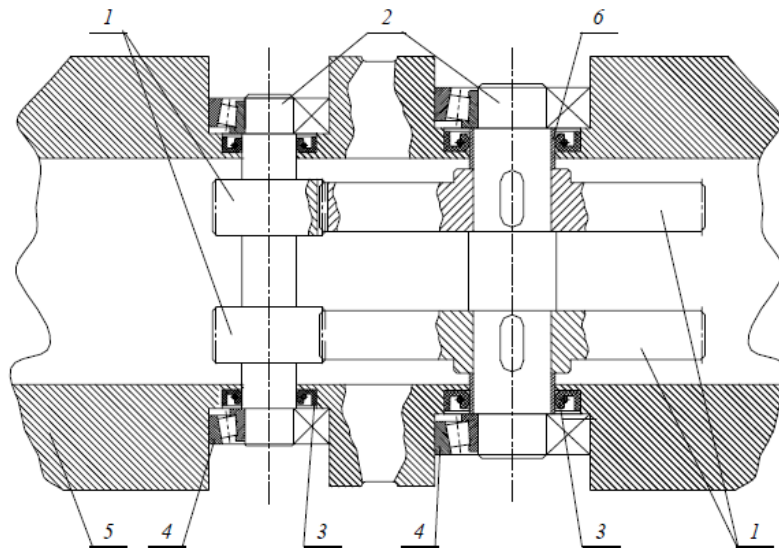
Конструктивна схема зубчастої передачі:
